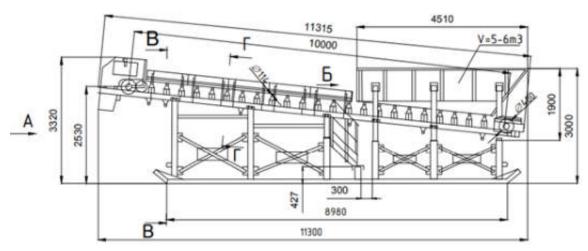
Передвижная породоотборочная установка (ППУ)
